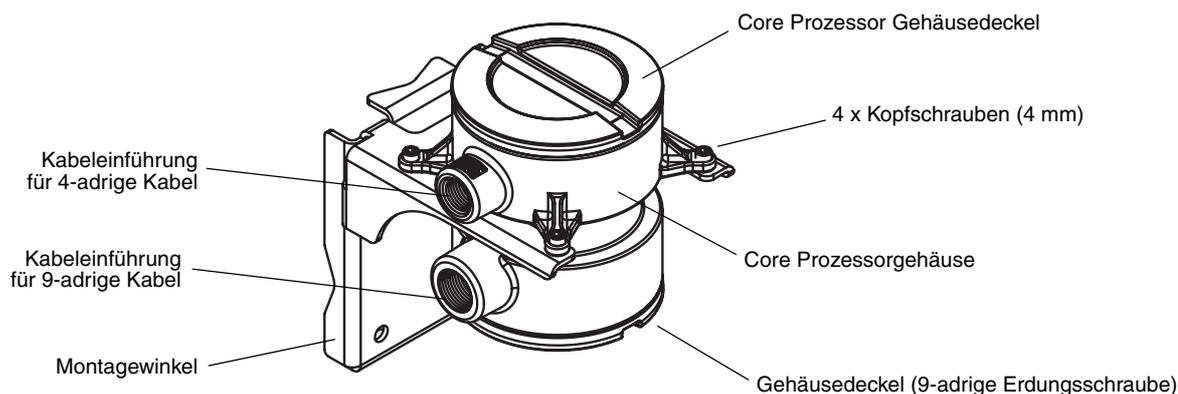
Externer Core Prozessor – Wandmontage oder Rohrmontage
